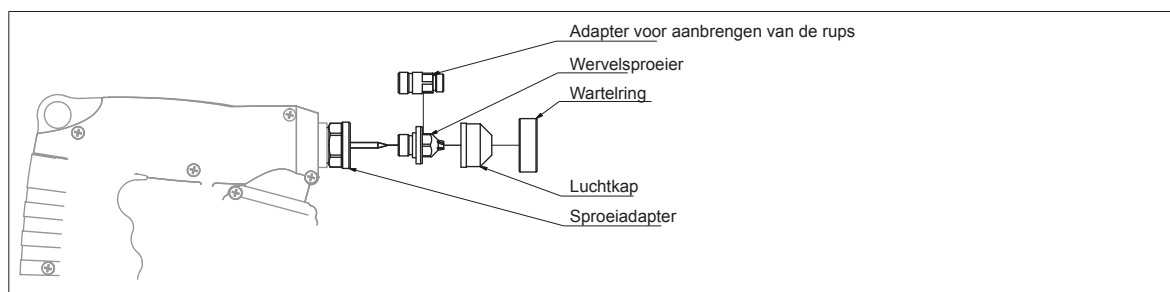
/11: Montage van de adapter voor aanbrengen van een rups
